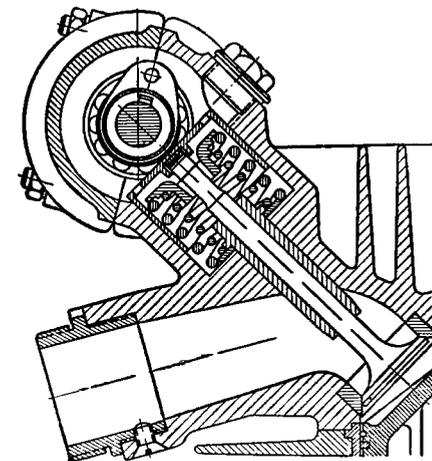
Стаканообразный толкатель, охватывающий пружины.
